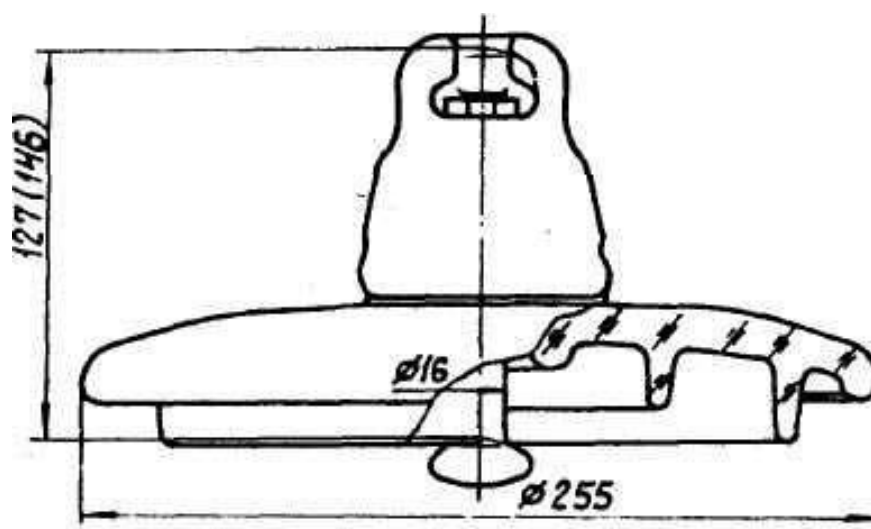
Чертеж изолятора ПС – 70Е
